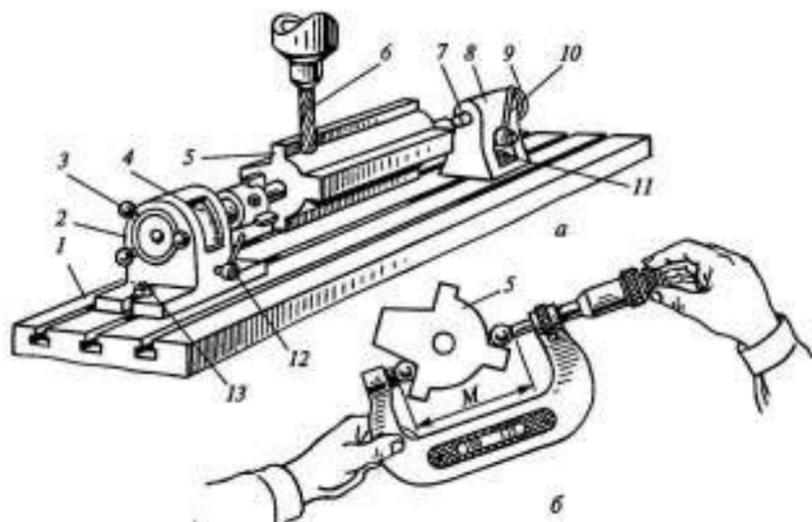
Обработка цилиндрической поверхности пуансона в делительном приспособлении:
